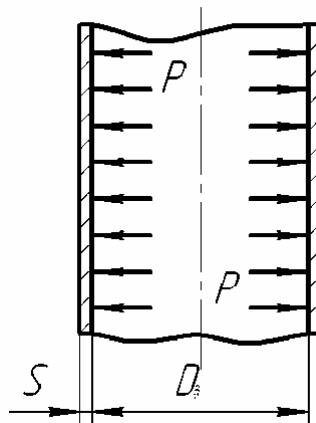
Розрахункова схема циліндричної обичайки
